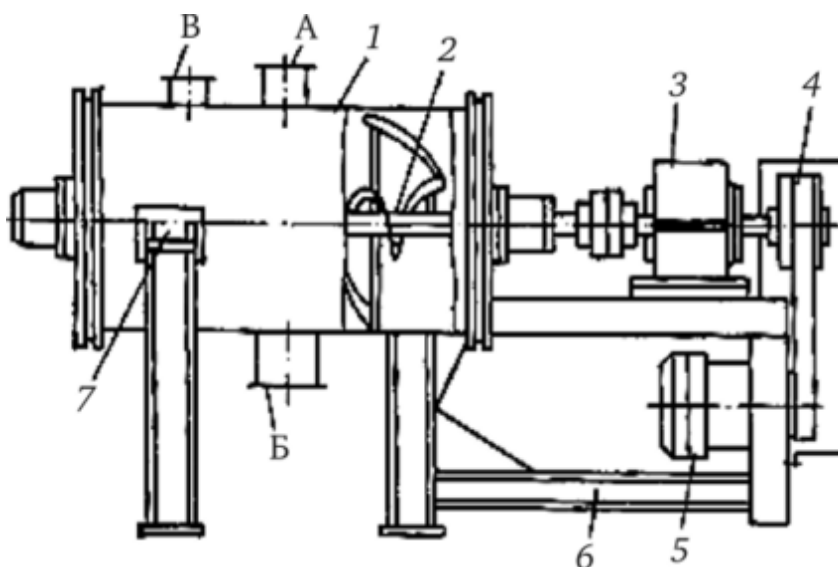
Барабанный змішувач з стрічкової мішалкою:
